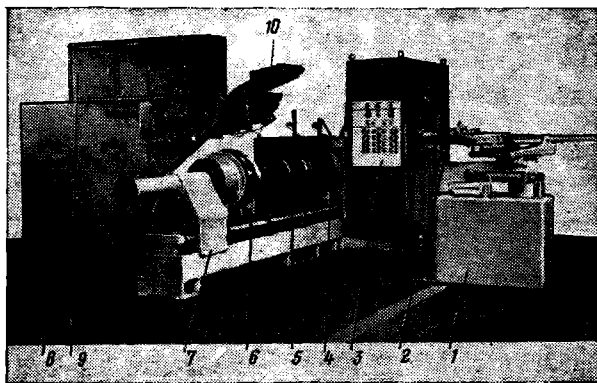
Схема станка Т-10 для второй стадии сборки покрышек:
